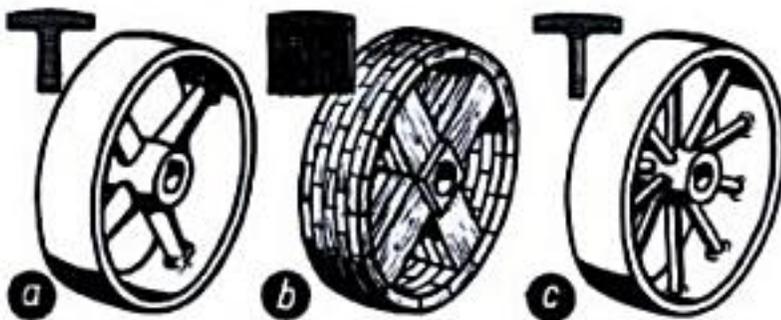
,1 Poleas de accionamiento: a) fundición gris; b) madera; c) acero (soldada)
